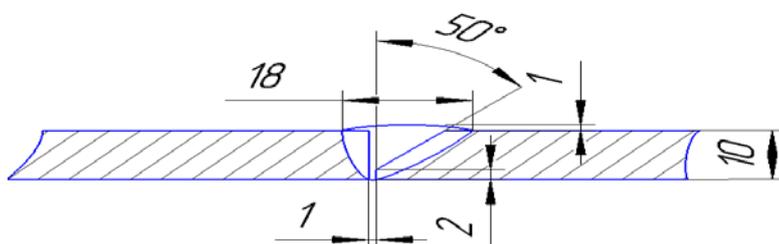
Эскиз стыковое сварное соединение ГОСТ 14771–76 С8 для сварки продольного стыка обечайки
